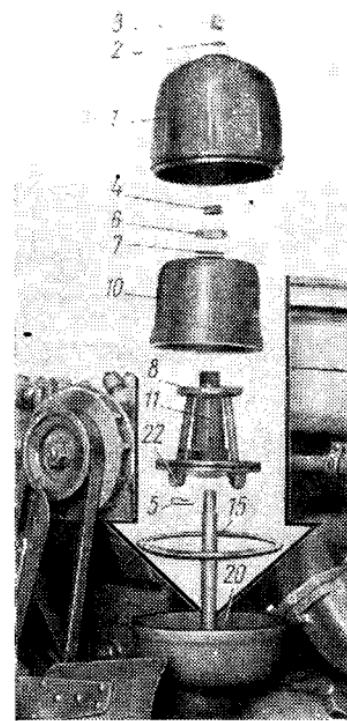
Порядок разборки фильтра центробежной очистки масла (позиции см. рис. 42)
